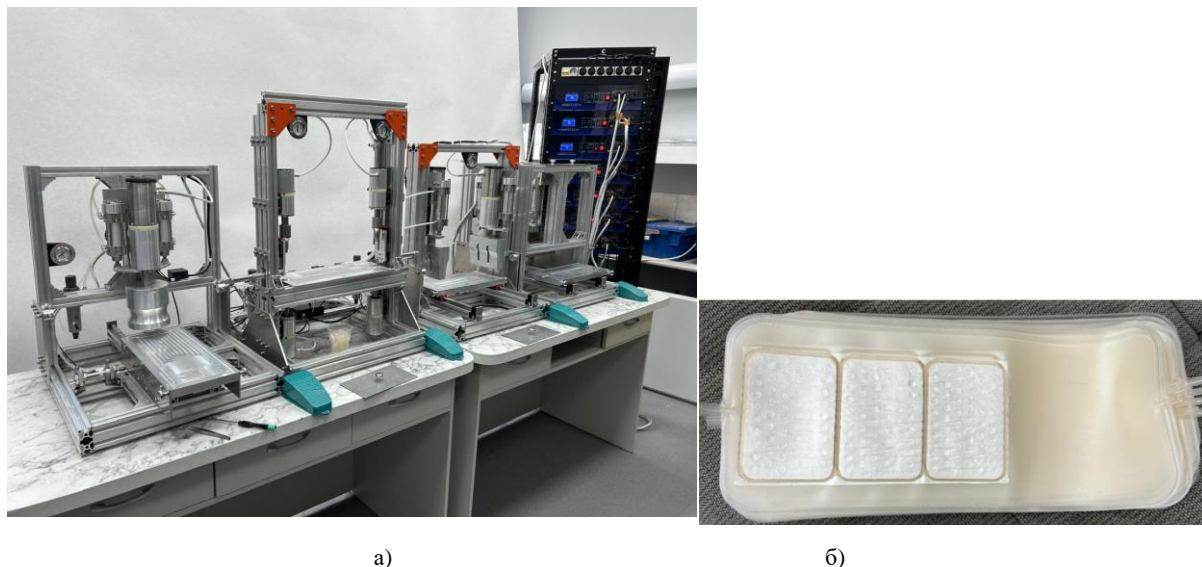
Фото установок для изготовления пластиковых контейнеров для забора и сушки компонентов крови
